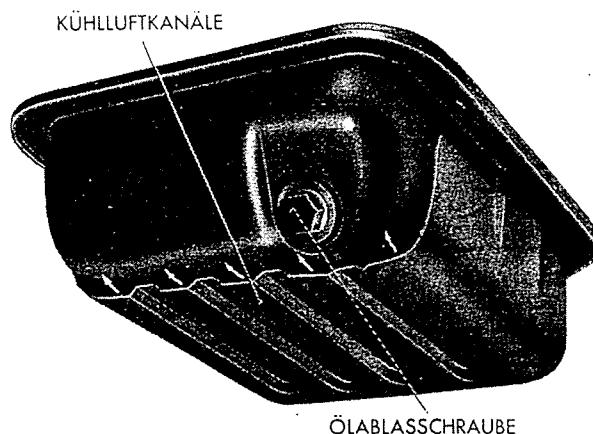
Motorölwanne mit Kühlluftkanälen.
